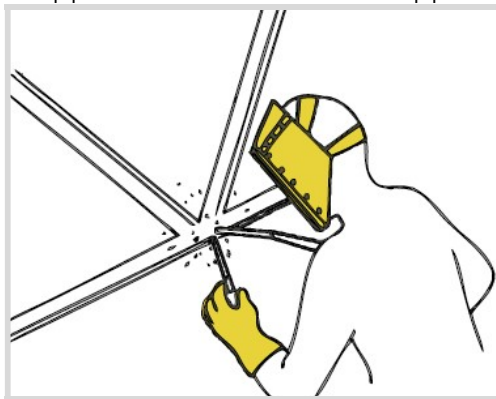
Corretto utilizzo dei DPI nelle fasi di saldatura
